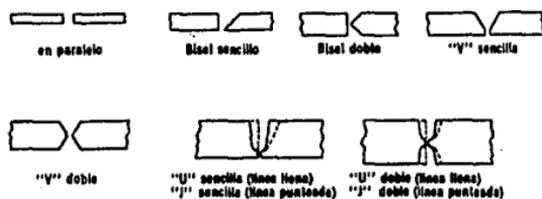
Formas de Soldaduras de Preparación.
